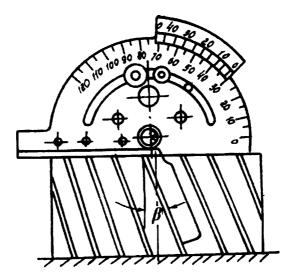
Измерение наклона спирали цилиндрической фрезы β с помощью универсального угломера
